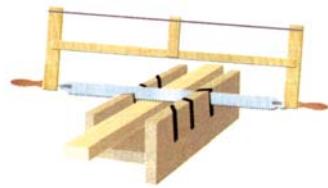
Пиление заготовки в стусле столярной ножковкой
